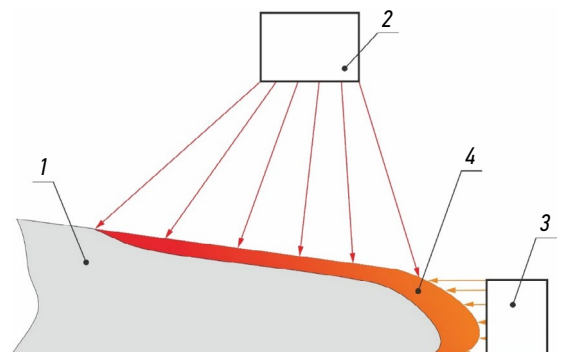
1 — обрабатываемый плоский образец; 2 — лазерный источник нагрева; 3 — индукционный источник нагрева; 4 — зона совместного действия двух источников нагрева.
